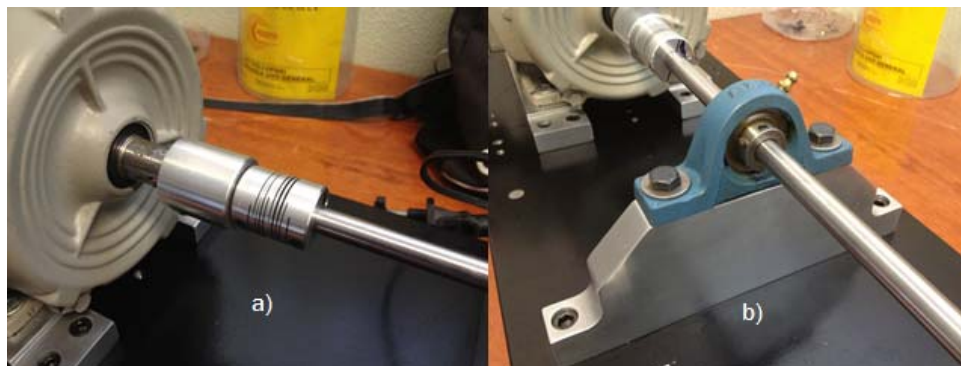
Colocación y ensamble de las piezas complementarias del prototipo. a) Ensamble de la flecha del motor, el buje, el cople y la flecha del prototipo. b) Ensamble de la base para rodamientos, rodamientos y flecha.
